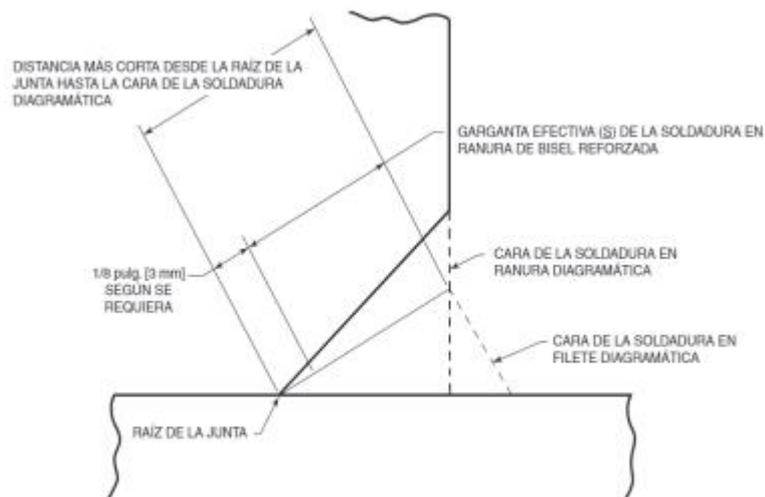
Soldadura en ranura de bisel con soldadura en filete reforzada (ver 4.4.2.7)
